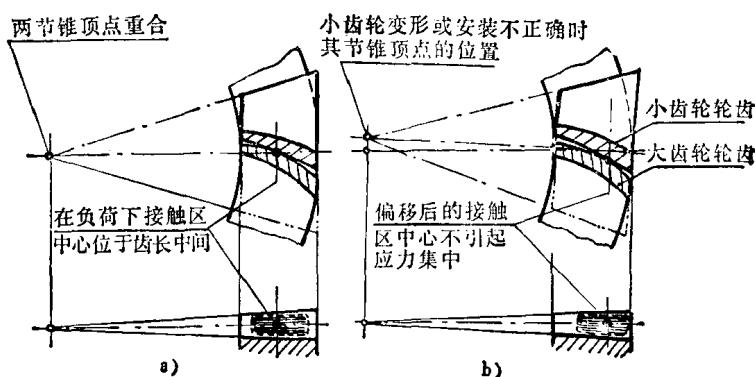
7 螺旋锥齿轮齿面的局部（点）接触，允许齿轮有某些相对位移
